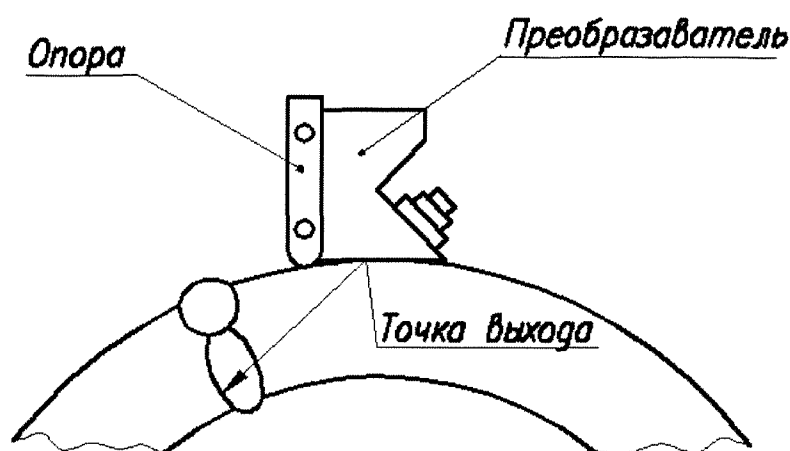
Опора и преобразователь в сборе на цилиндрической поверхности
